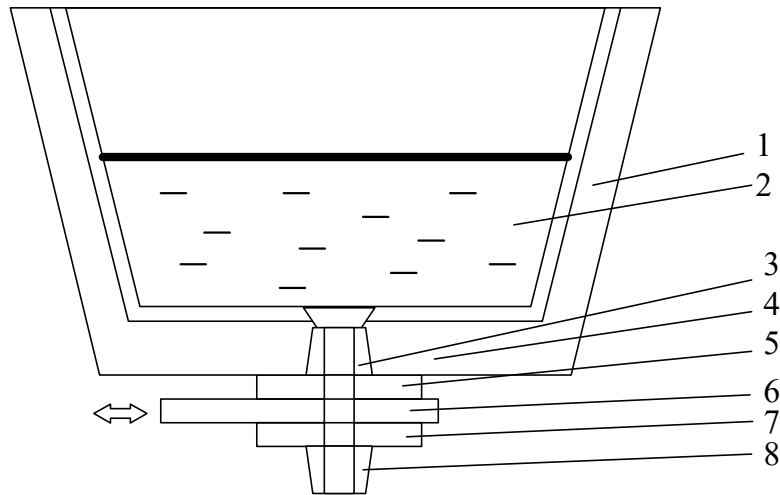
Общий вид сталеразливочного ковша: 1 - рабочий слой стен ковша; 2 – жидкий металл; 3 - верхний стакан разливочного узла; 4 – днище стальной ковша; 5 – верхняя плита шиберного затвора; 6 – подвижная плита шиберного затвора; 7 – нижняя плита шиберного затвора; 8 – нижний стакан разливочного узла.
